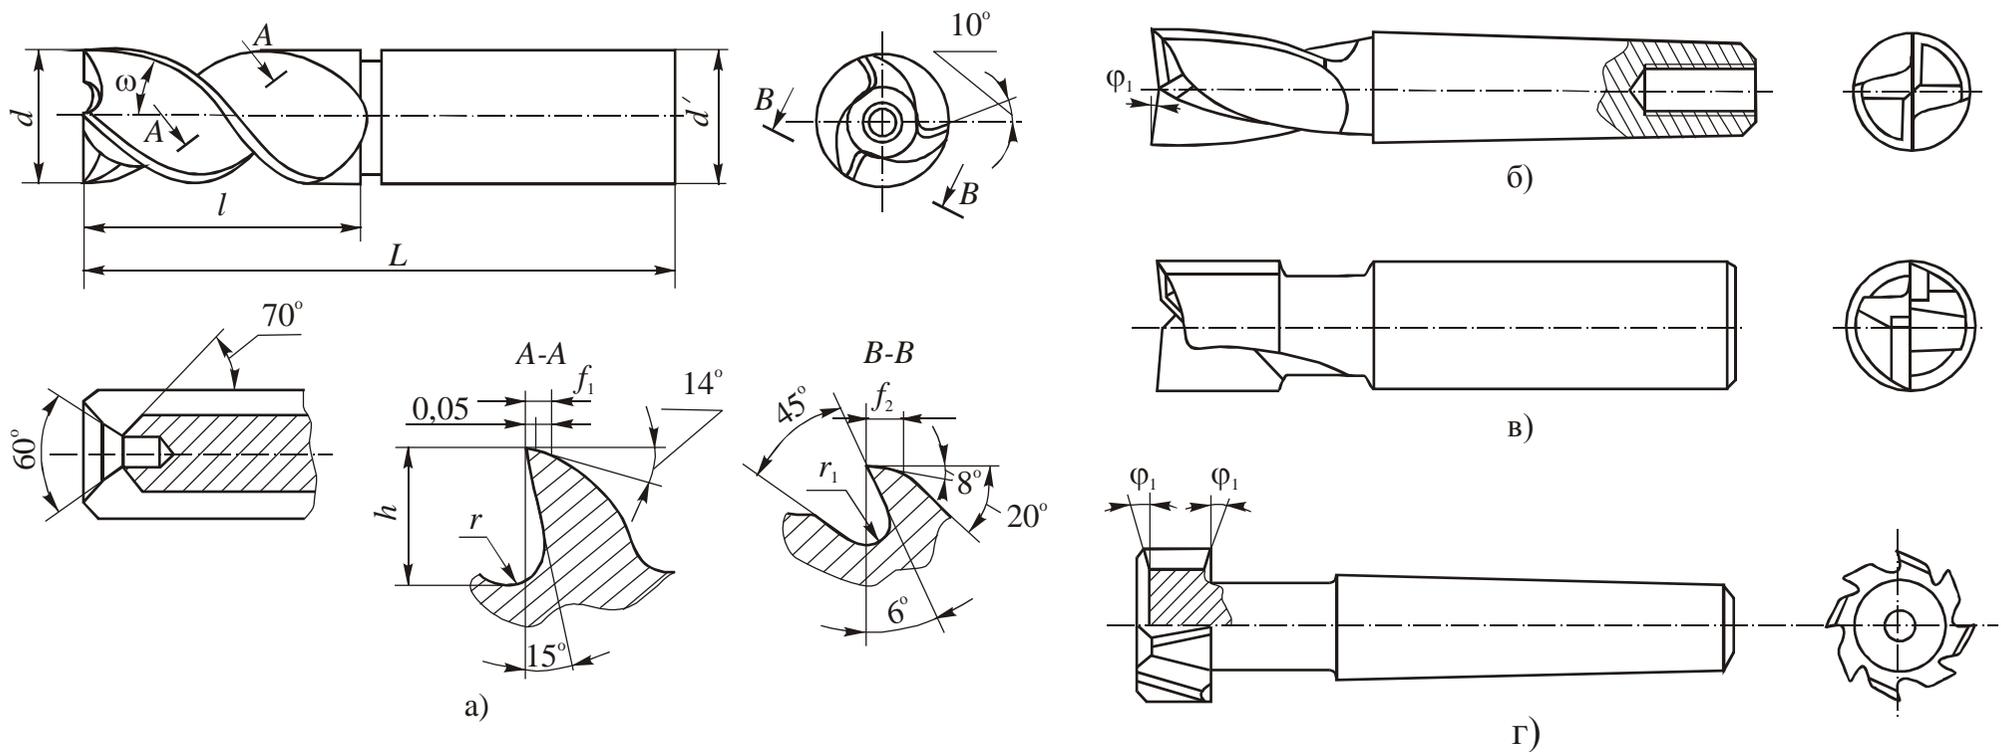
Фрезы концевые: *а* – стандартная концевая фреза; *б* – шпоночная фреза из быстрорежущей стали; *в* – шпоночная фреза с напайными твердосплавными пластинами; *г* – фреза для обработки Т-образных пазов
